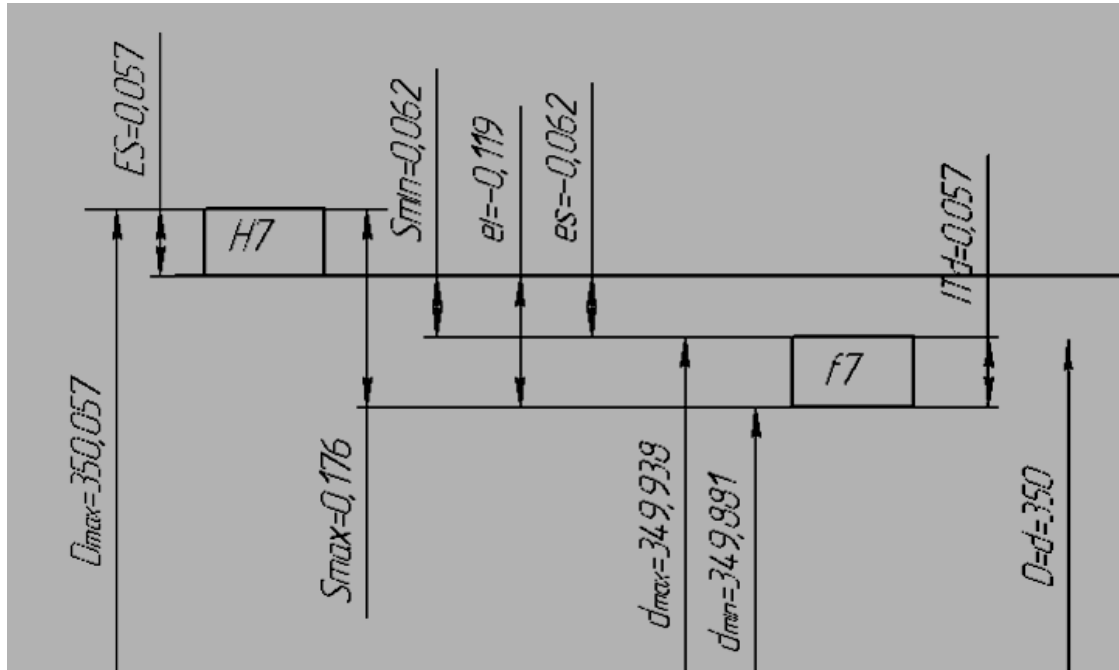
Схема полей допуска соединения  $\varnothing 350H7/f7$
